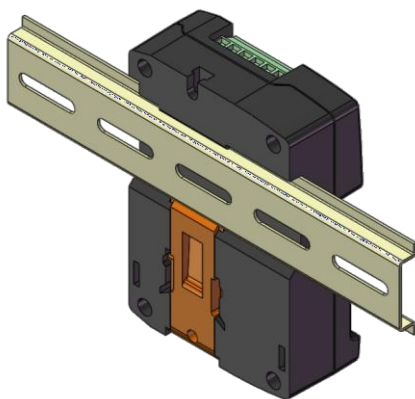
Встановлення напрямної рейки CMM366A-ET
